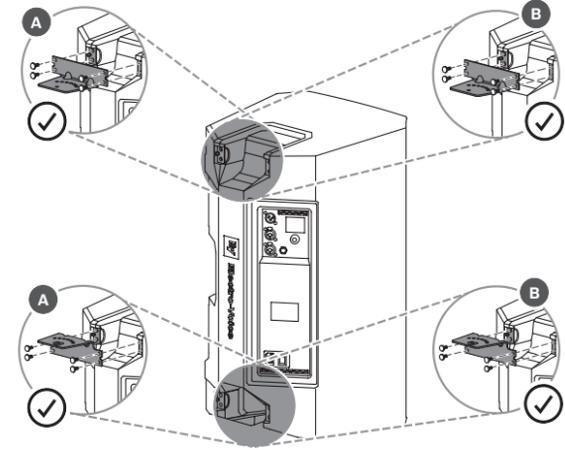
Instalação correta da placa de montagem superior e inferior em versões de 15 polegadas
